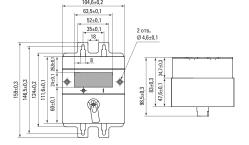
Габаритные размеры моторного привода к ВА-99М 250
